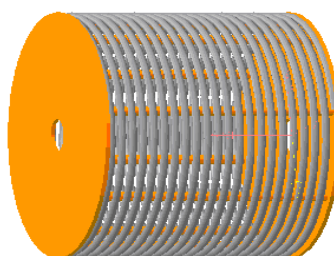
Циліндричний барабан з прутковою поверхнею
